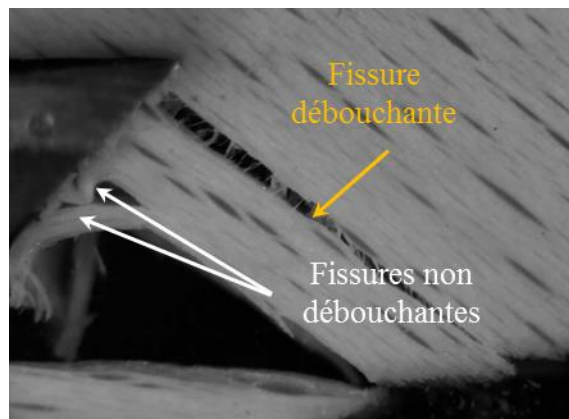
Fissures débouchante et non-débouchantes dans le cadre d'essais de rabotage en coupe 90° - 37°.
